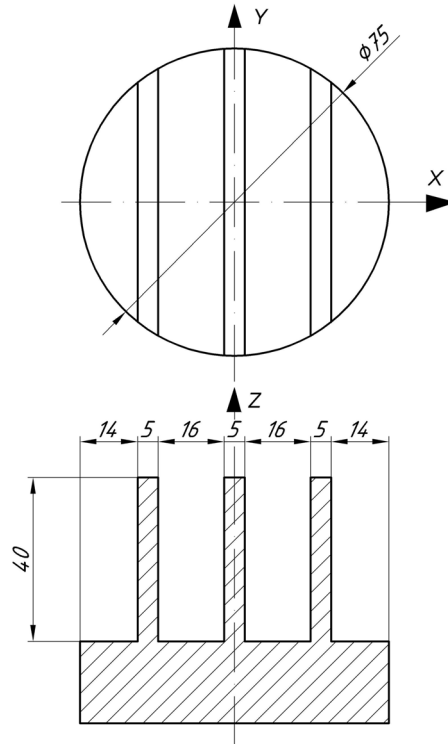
Ескіз заготовки з алюмінієвого сплаву
